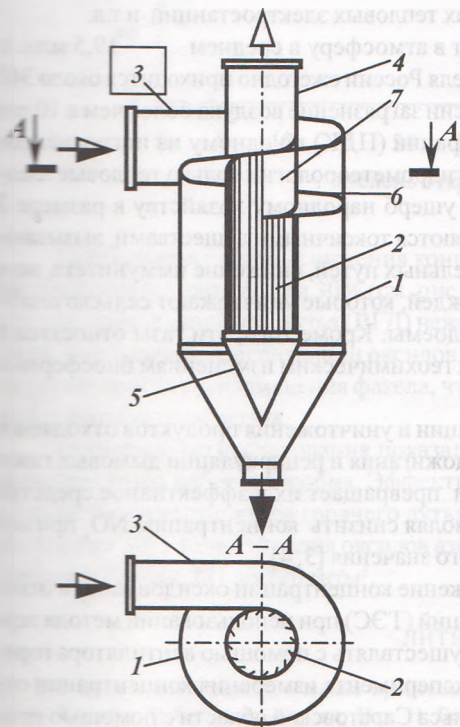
Усовершенствованный центробежно-инерционный пылеуловитель: 1 – корпус; 2 – жалюзийная решетка; 3 – выходной патрубок; 4 – патрубок отвода чистого воздуха; 5 – днище решетки; 6 – направляющая перегородка; 7 – лист
